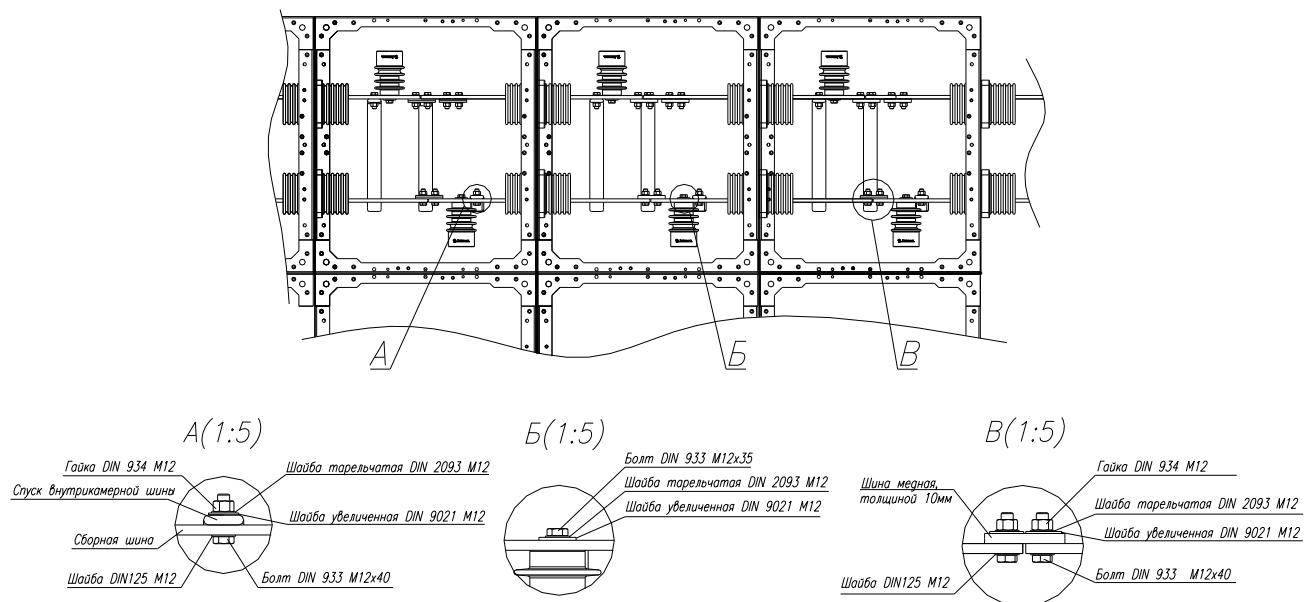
Монтаж сборных шин 1600 А (вид сверху на шкафы КРУ)
